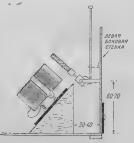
, Крепление катушки L_1 и устройство подвижного станочка для катушки обратной связи.
